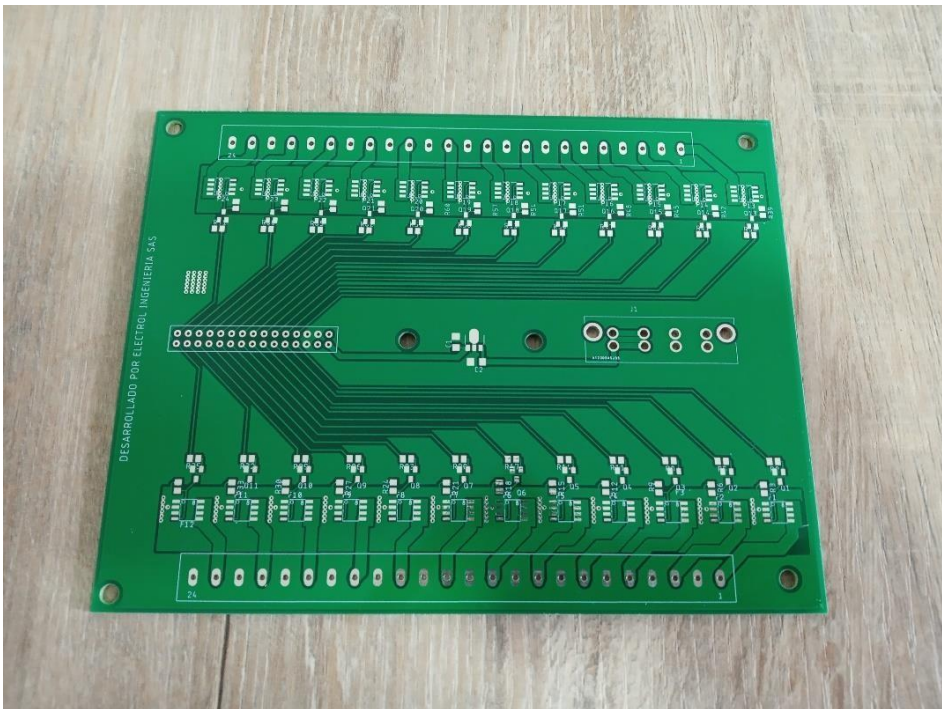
Tarjeta DC PCB secuenciador de luces [Vista superior]. Tobón. (2019)
